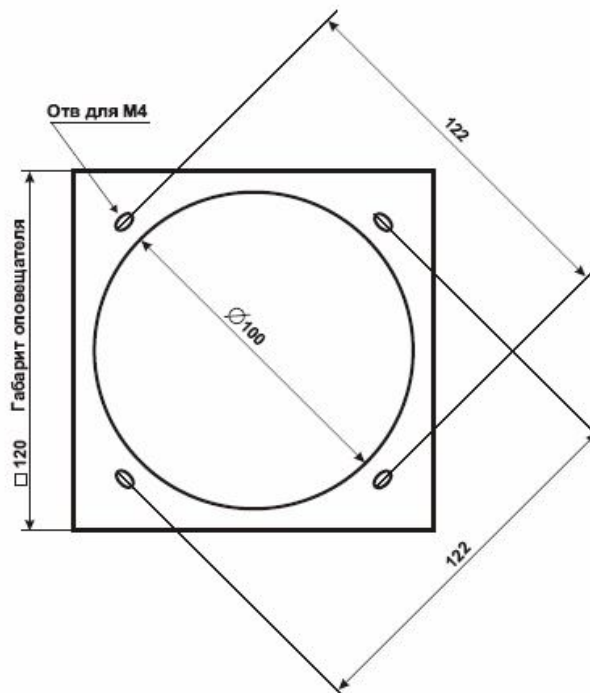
Габаритные размеры монтажной пластины SMP и размеры потолочных отверстий для установки оповещателей.
